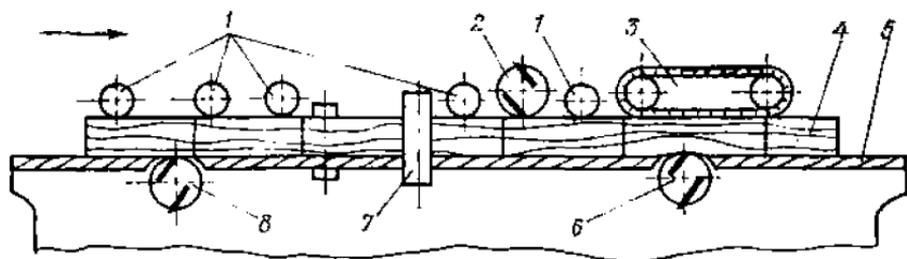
Схема обработки заготовки на четырехстороннем продольно-фрезерном станке с фуговальным устройством:
